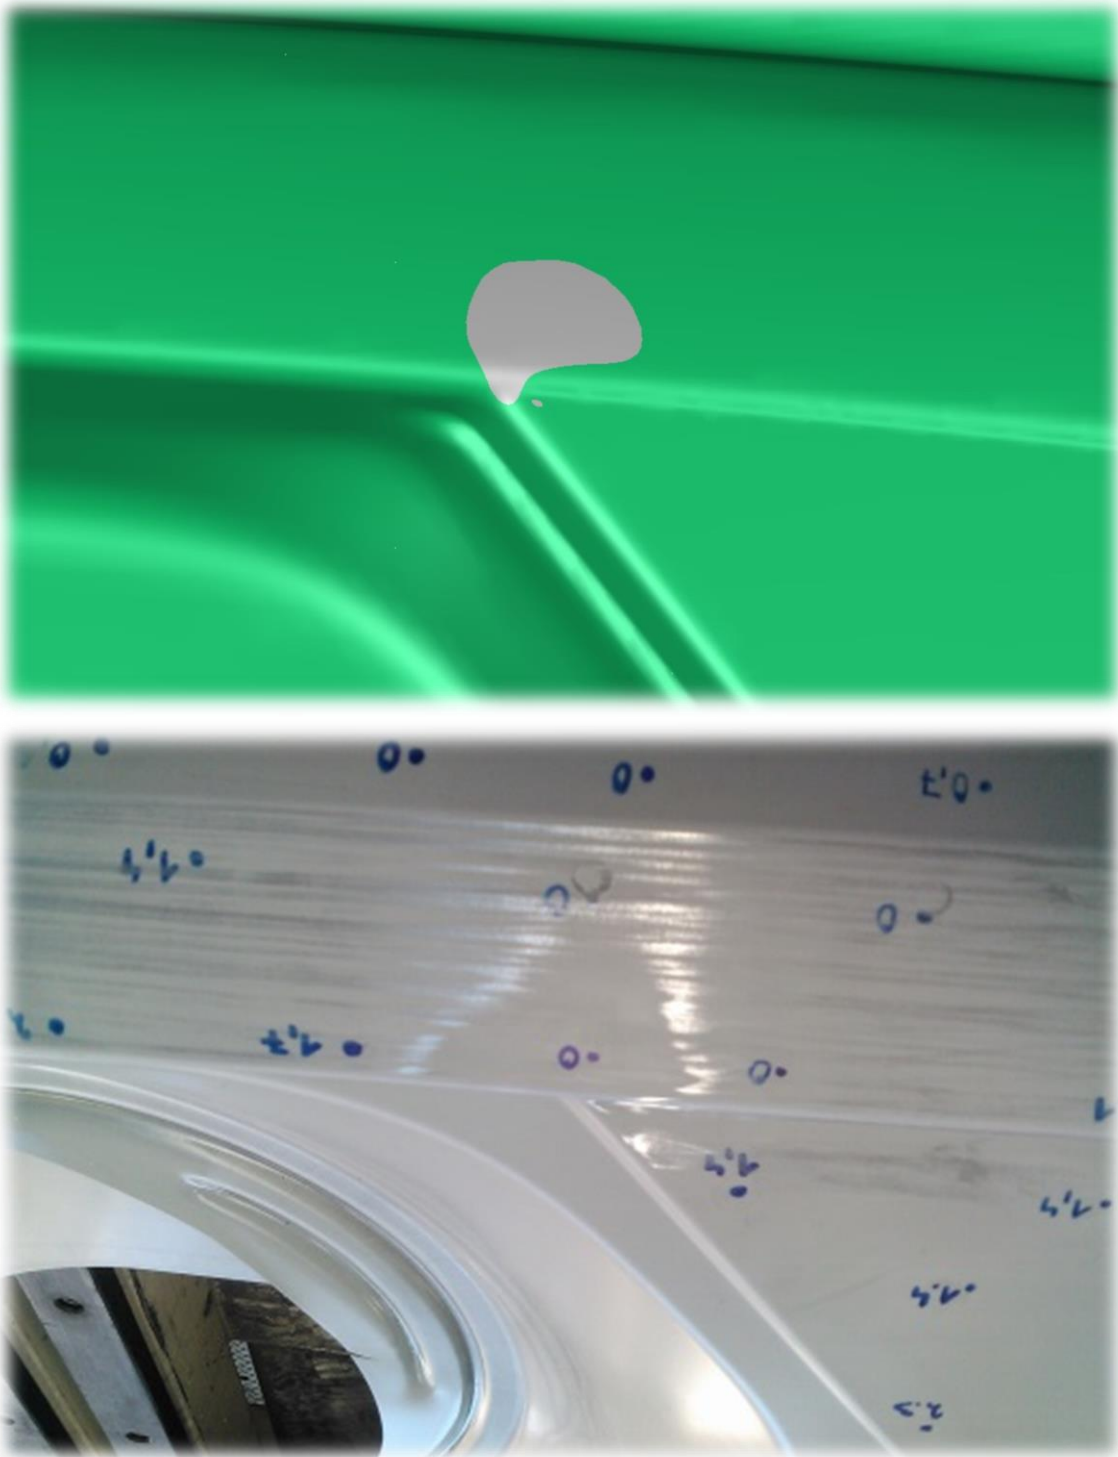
Odpružení spodních pátých dveří (plech DC 06, tloušťka 0,7 mm)
